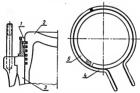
Приспособления пля опускания поршия с кольцами в цилиндр:
